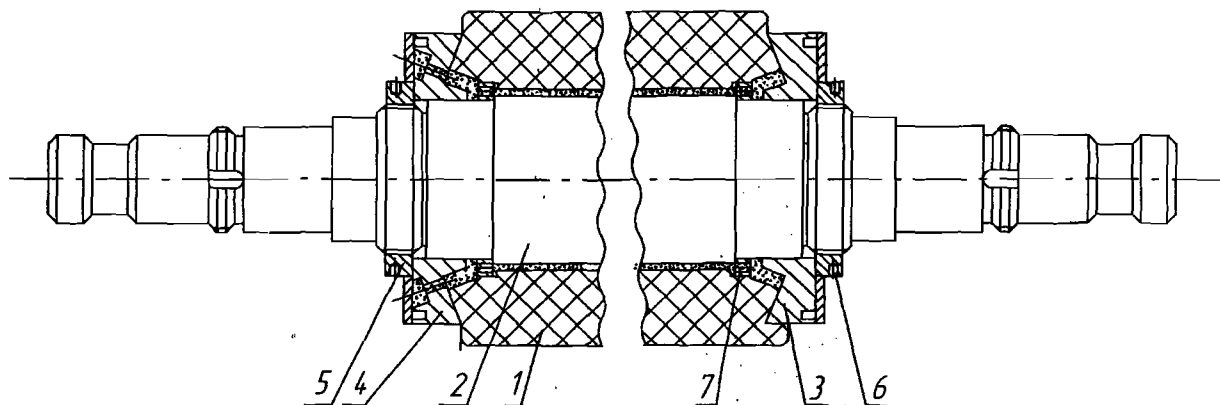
Гранитный вал: 1 – гранитный цилиндр; 2 – стальной сердечник; 3,4 – шайба; 5,6 – гайка; 7 – центрирующая втулка
